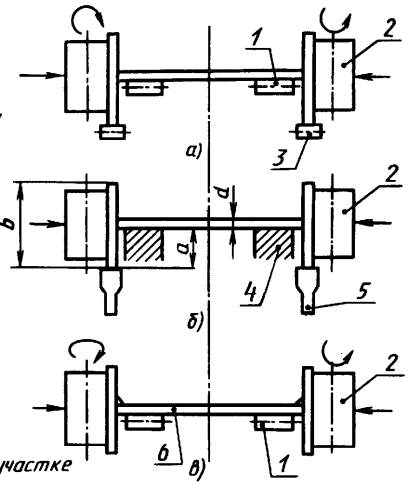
Схемы расположения опорных баз и прижимов сборочного стана
